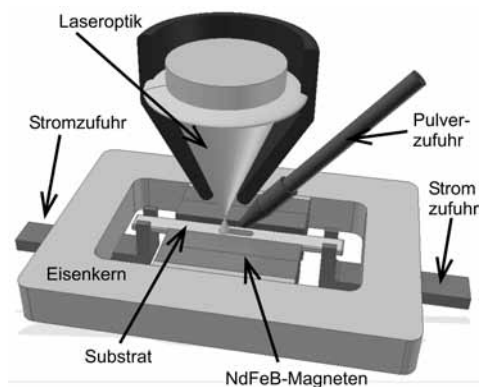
Aufbau zum magnetisch gestützten Laserstrahlaufragschweißen
